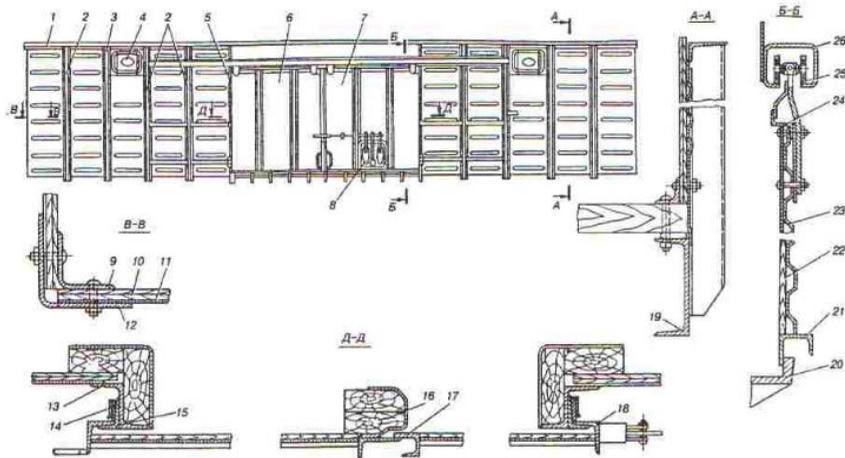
Боковая стена кузова универсального крытого вагона
